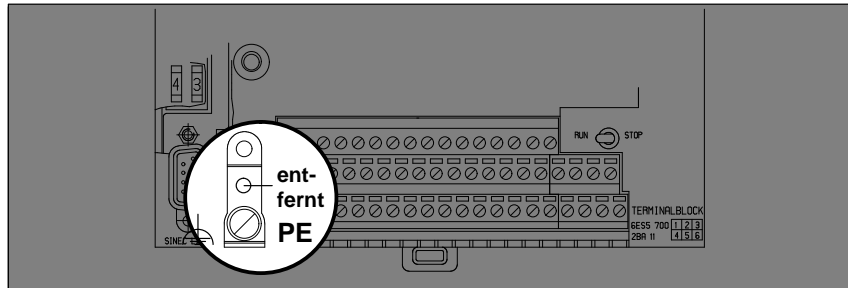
Obere Schraube entfernt bei erdfreiem Aufbau
